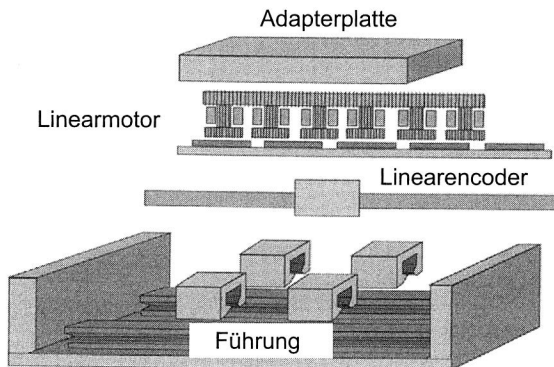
Prinzipieller Aufbau einer Vorschubachse mit Linearmotor [46]
